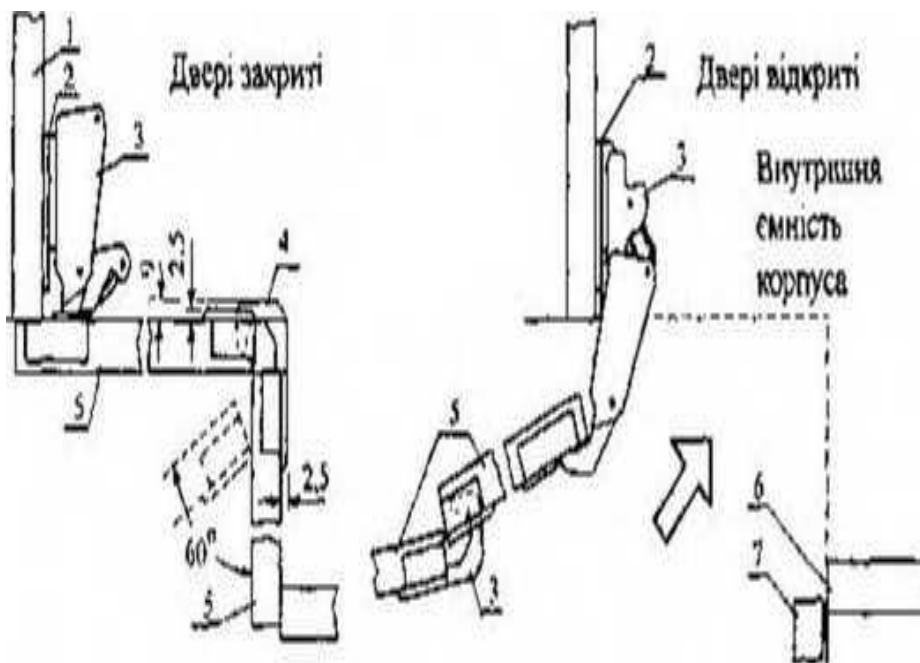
Установка дверей із внутрішнім кутом ємності корпусу: 1 - стінка бічка, 2 –прокладка, 3 - кутова завіса з широким розкриттям, 4 - кутова завіса, 5 - дверні полотна, 6 - середня стінка, 7 - двері наступної ємності корпусу (Hafele).
